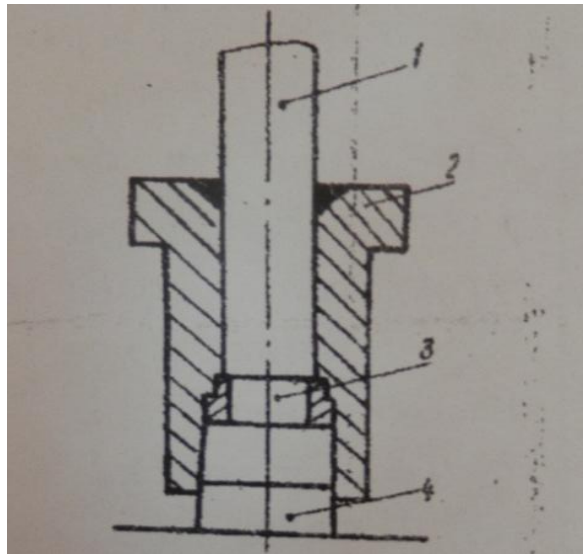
Устройство для запрессовки пека в кольцо:
